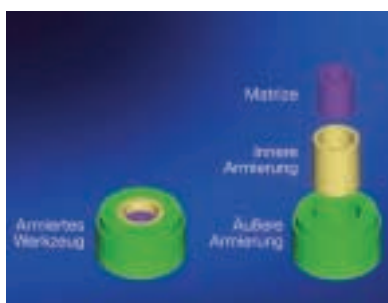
Armierungsverband eines Kaltumformwerkzeugs
